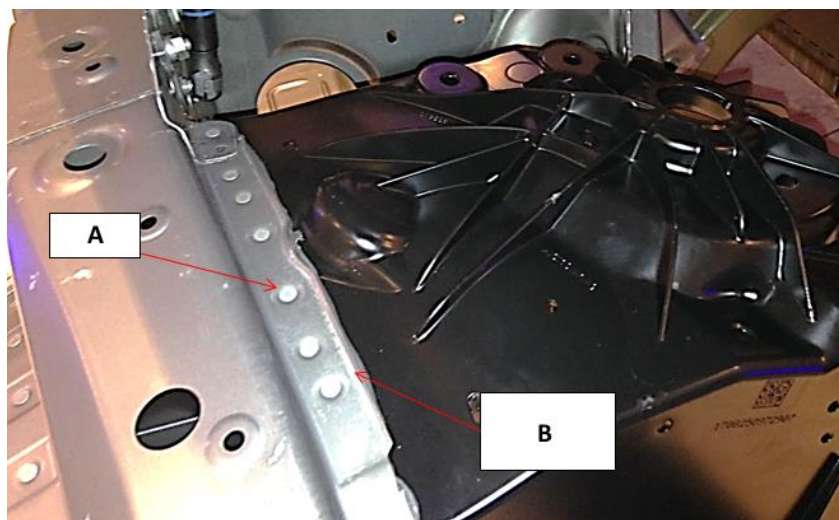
SPR y adhesivo estructural en una carrocería de automóvil: A. SPR, B. Adhesivo estructural. Fuente: TWI
